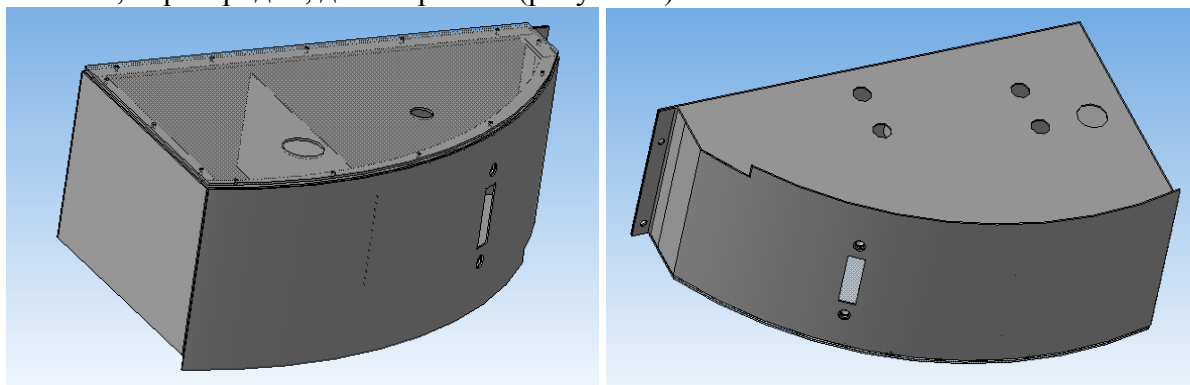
Сборочная 3D-модель стенок, перегородок, дна и крышки бака
